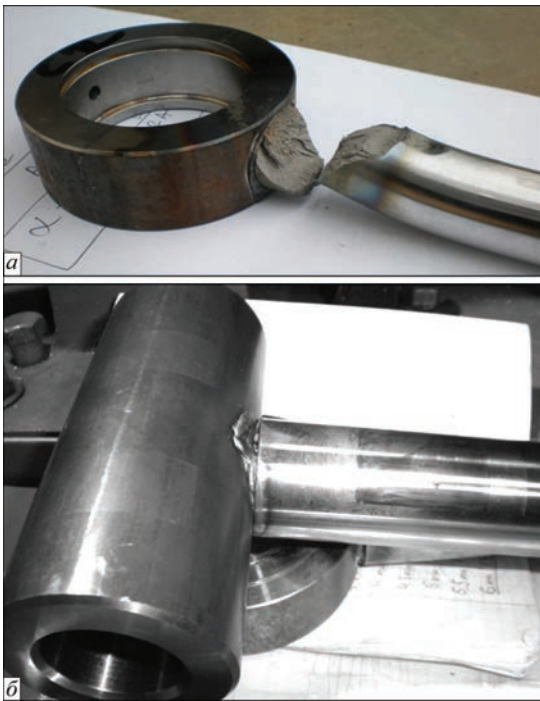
Сварной шток Ш25, выполненный КСС сопротивлением по схеме 1, после испытаний на загиб (а); шток, выполненный по схеме 2 (б)
